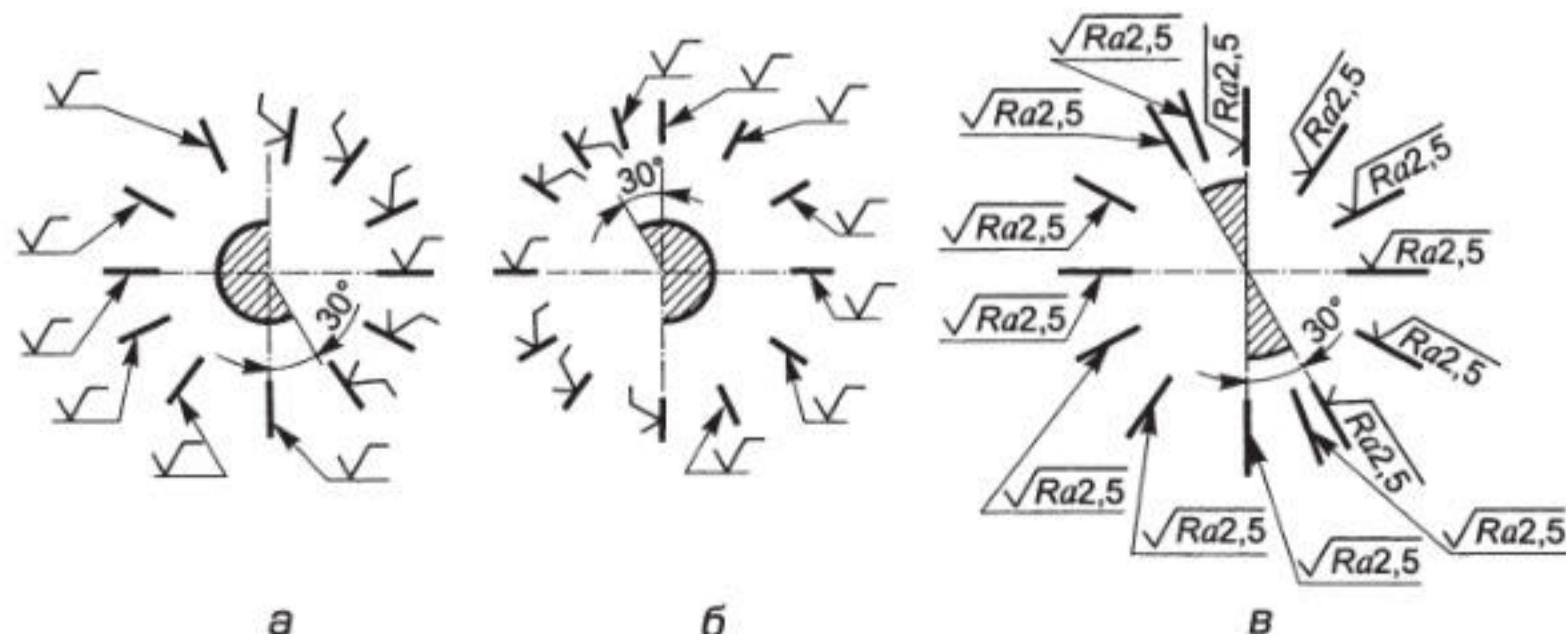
Расположение обозначений шероховатости поверхности:
